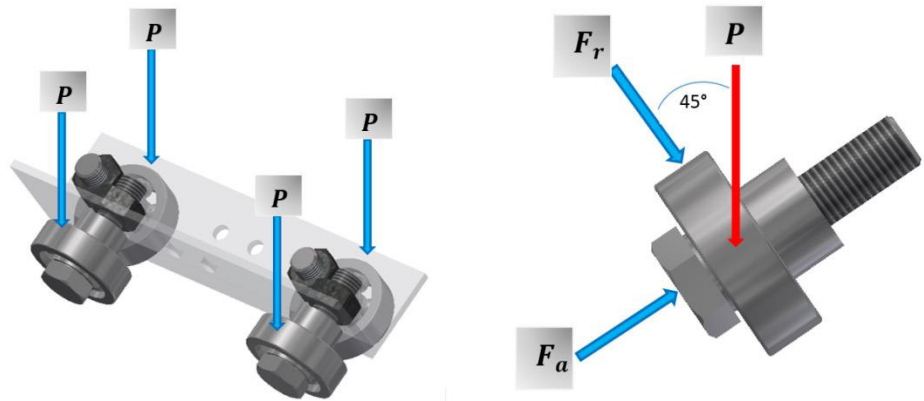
Distribución de fuerzas sobre cada rodamiento.
